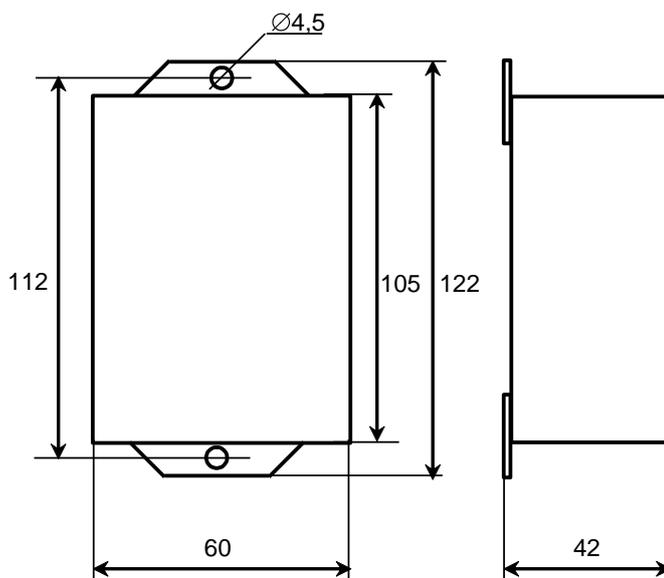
Габаритные и установочные размеры ПИ
